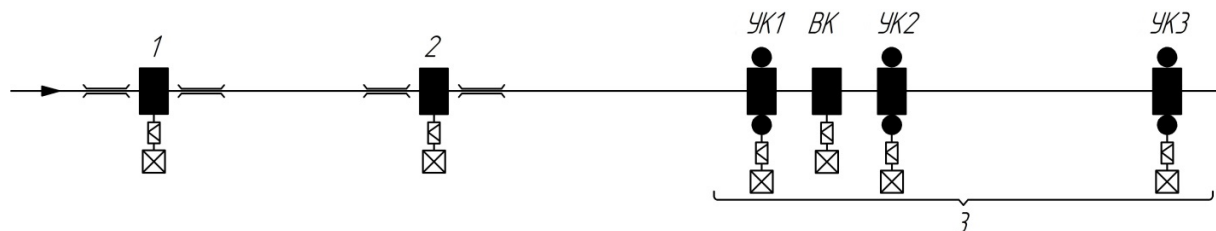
Схема расположения рабочих клеток современного типового рельсобалочного стана: 1 и 2 – обжимная и черновая реверсивные клетки дуо; 3 – чистовая непрерывно-реверсивная группа: УК1, УК2 универсальные реверсивные клетки; УК3 – чистовая неререверсивная клеть; ВК – двухвалковая сдвигаемая вспомогательная клеть
